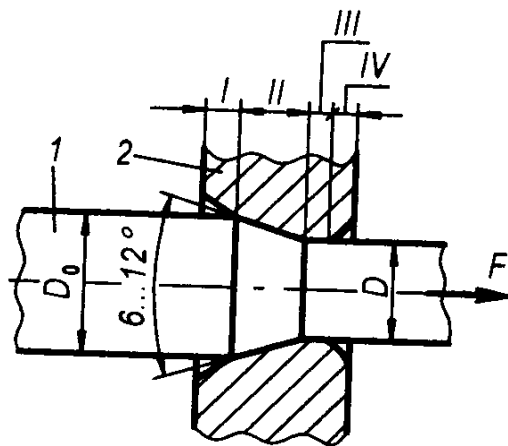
Схема волочіння: 1 – заготовка; 2 – волока; I – вхідна; II – деформувальна, III – калібрувальна, IV – вихідні зони; D_0 і D – діаметри заготовки до і після волоки відповідно; F – тягова сила
